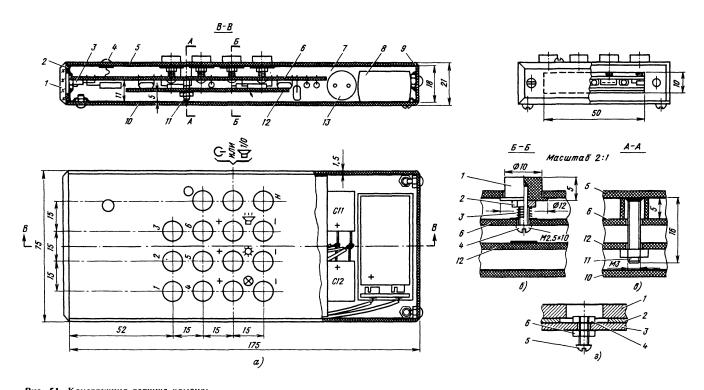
Конструкция датчика команд: a — расположение плат в корпусе (I — стекло; 2 — передняя стенка; 3 — излучающие диоды; 4 — контрольный светодиод; 5 — верхняя стенка; 6 — основная плата; 7 — боковые стенки корпуса; 8 — батарея; 9 — задняя стенка; 10 — дно; 11 — шпильки крепления; 12 — контактная плата; 13 — конденсаторы); 6 — конструкция кнопочного узла; (1 — кнопка; 2 — гайка; 3 — пружина; 4 — контактный винт; 6 — основная плата; 12 — контактная плата); 6 — крепление плат в корпусе (обозначения аналогичны рис. 51,a); c — форма для литья кнопок
